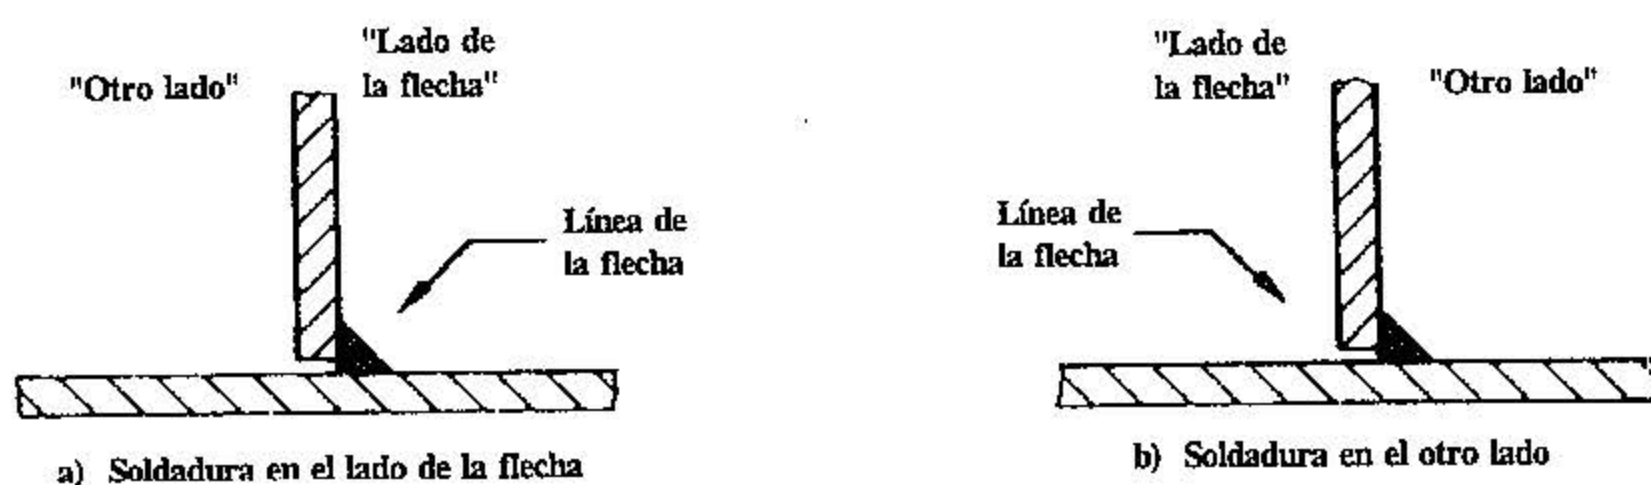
Unión en T con una soldadura en ángulo
